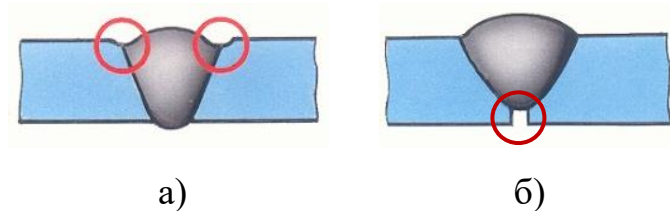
Схема підрізання (а) та непроварювання (б) шва
